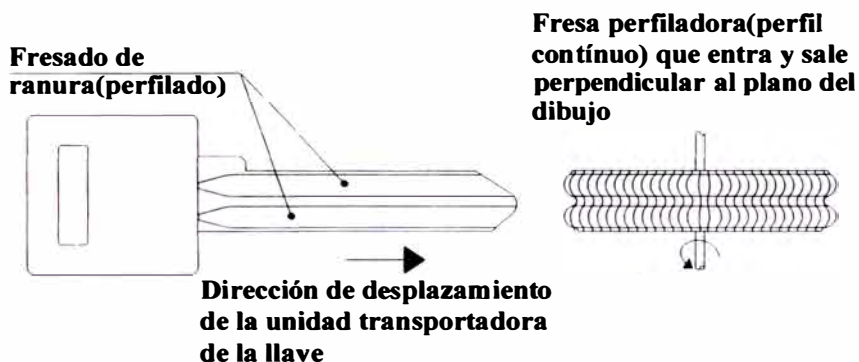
Vista de planta de llave e ingreso de fresa perfiladora
